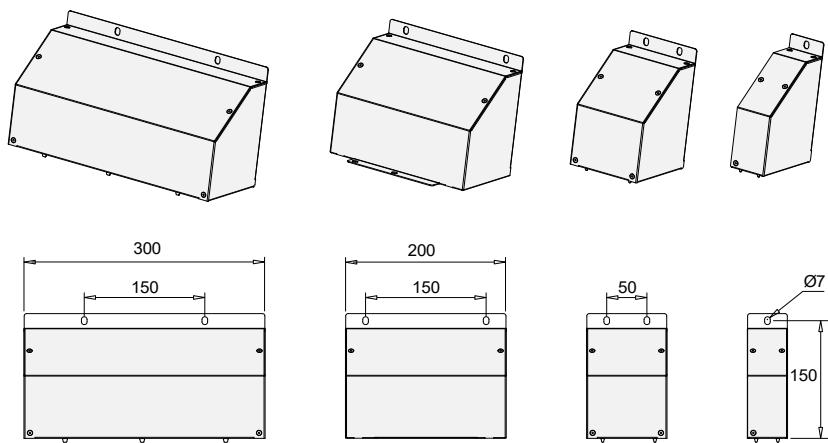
Габаритные размеры теплоизоляционной перегородки (миллиметры)
